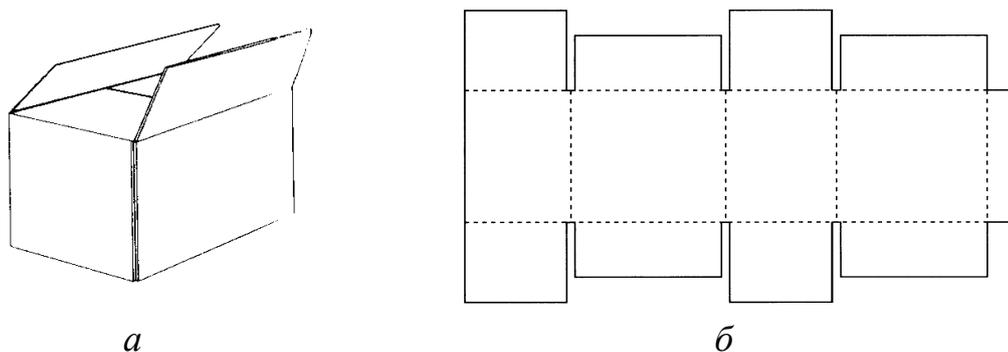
Внешний вид (а) и развертка (б) ящика с четырьмя клапанами
